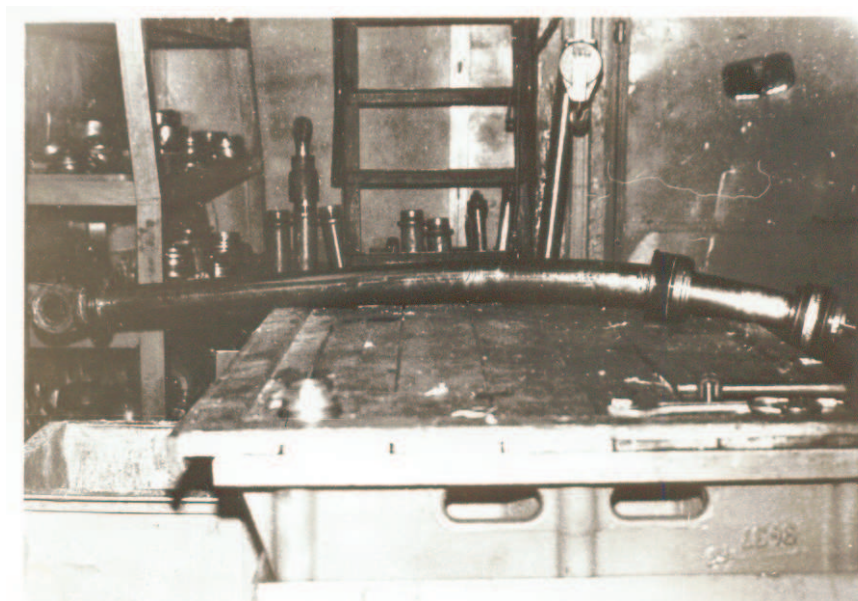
Деформация штока гидроцилиндра рукоятки одноковшового экскаватора
